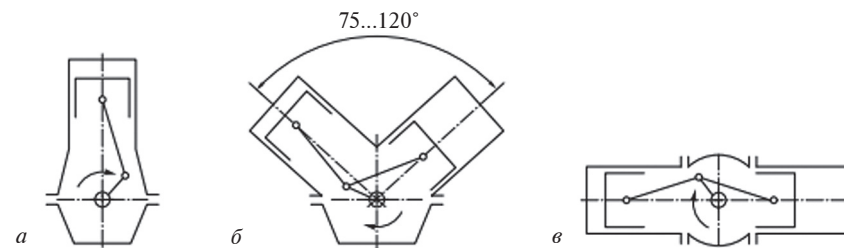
Схемы расположения цилиндров двигателей: а – рядное вертикальное; б – двухрядное V-образное; в – оппозитное
